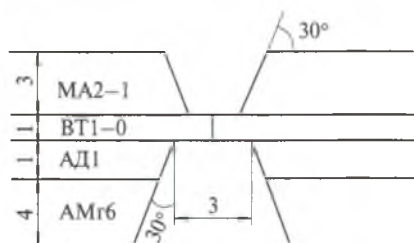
Схема подготовки кромок для сварки многослойного материала
